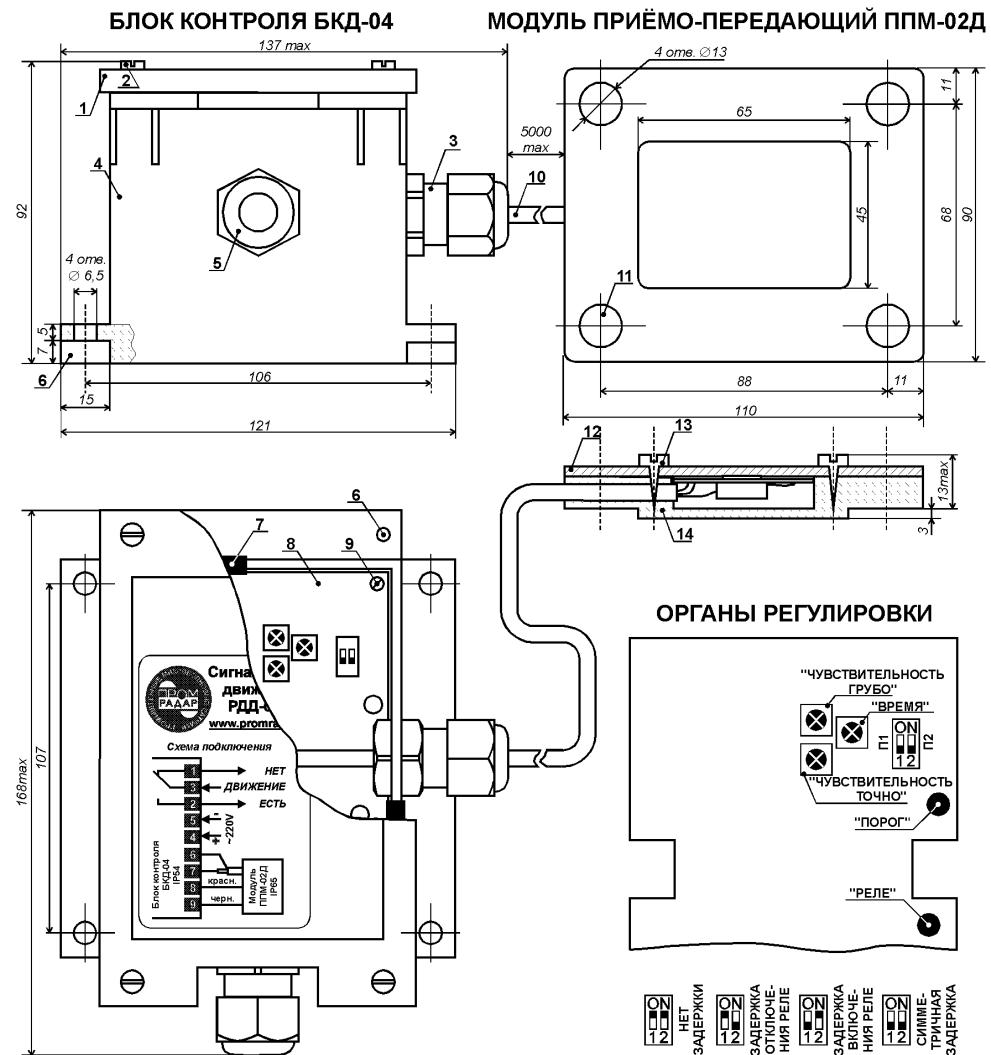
Конструкция и органы управления сигнализатора движения РДД-04.
